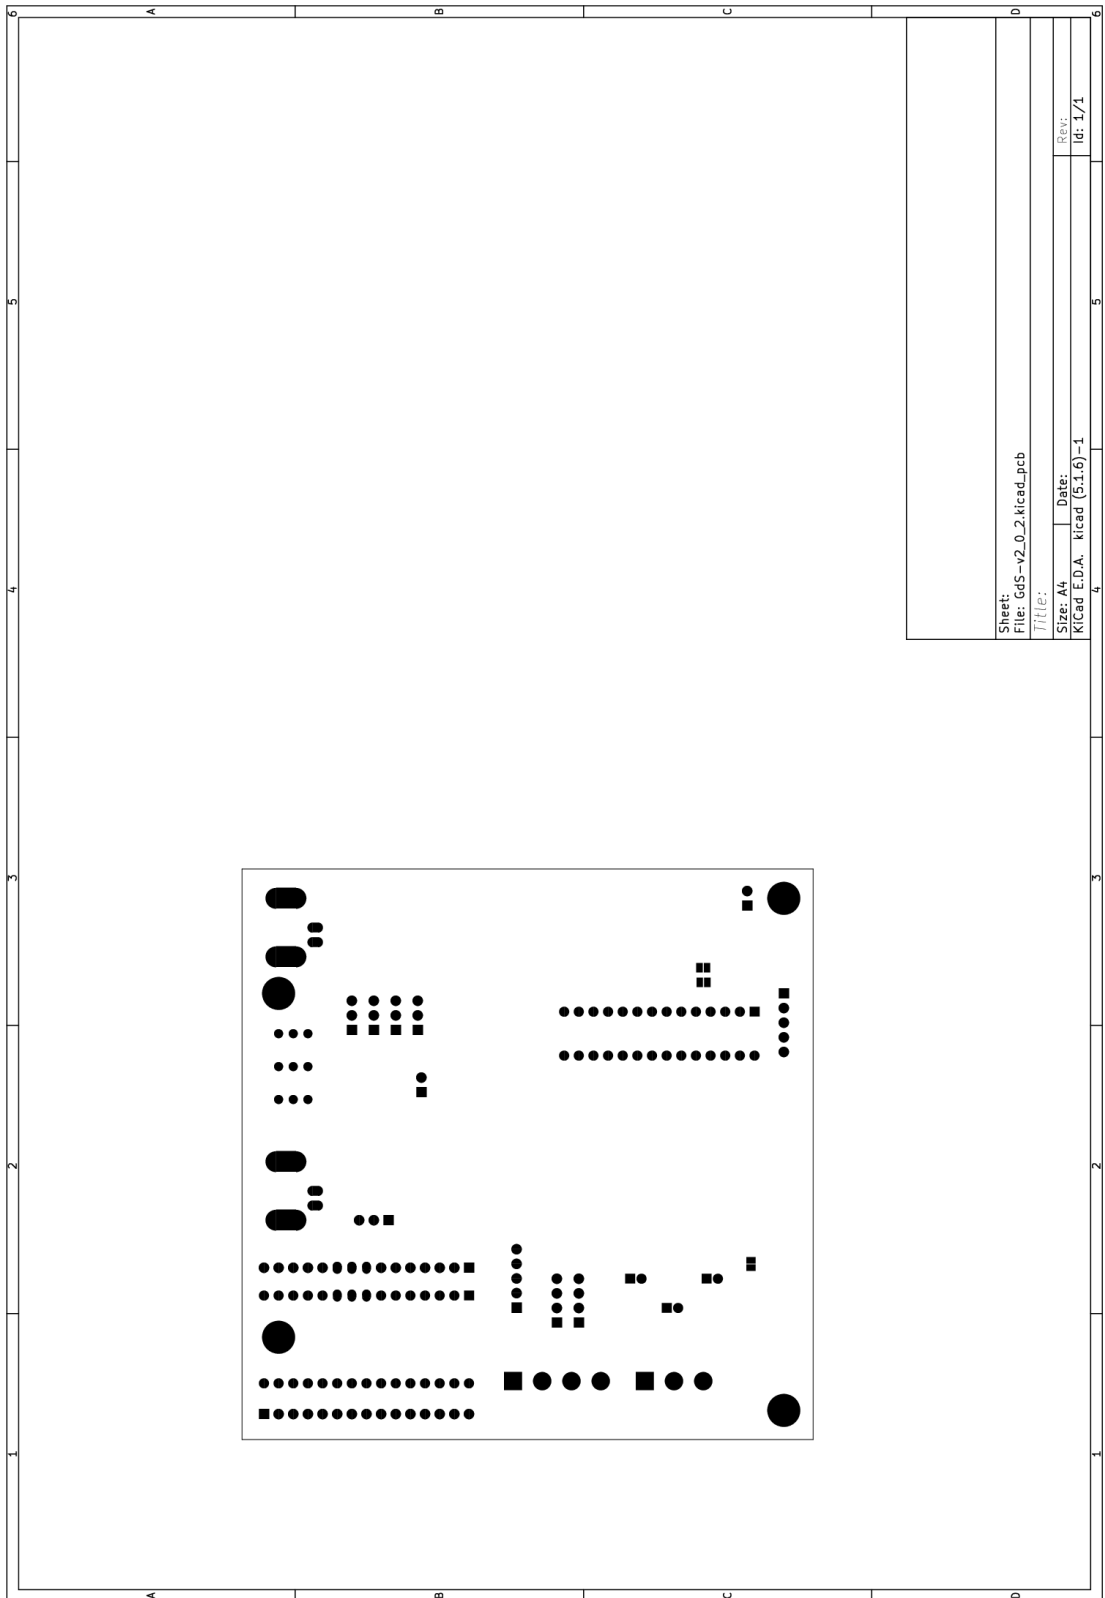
PCB máscara de soldadura (vista inferior).
